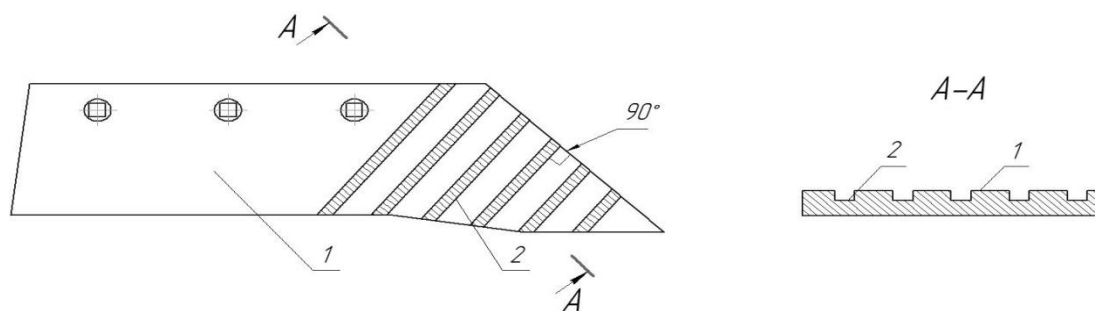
Плужный лемех (лемех конструкции Брянской ГСХА): 1 - рабочая поверхность, 2 - пазы на рабочей поверхности
